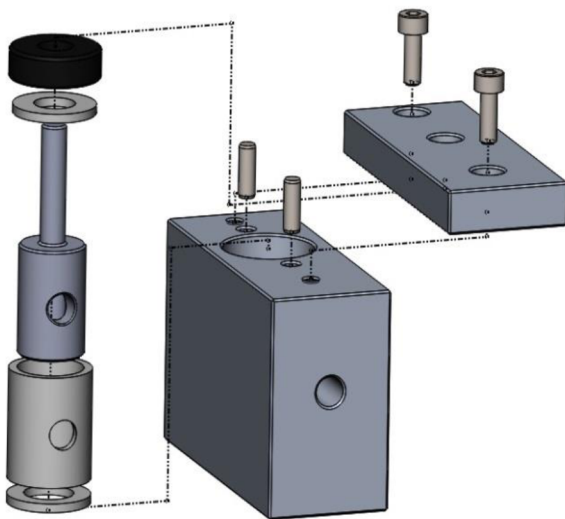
Vista explodida da válvula de gaveta rotativa [1]
